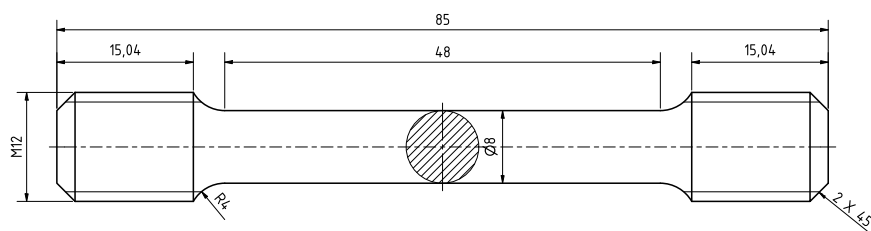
Technische Zeichnung der verwendeten B8x40-Rundzugprobe, Maße in mm
